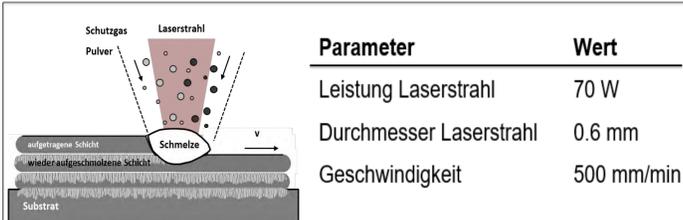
Verfahrensprinzip Laserauftragschweißen
